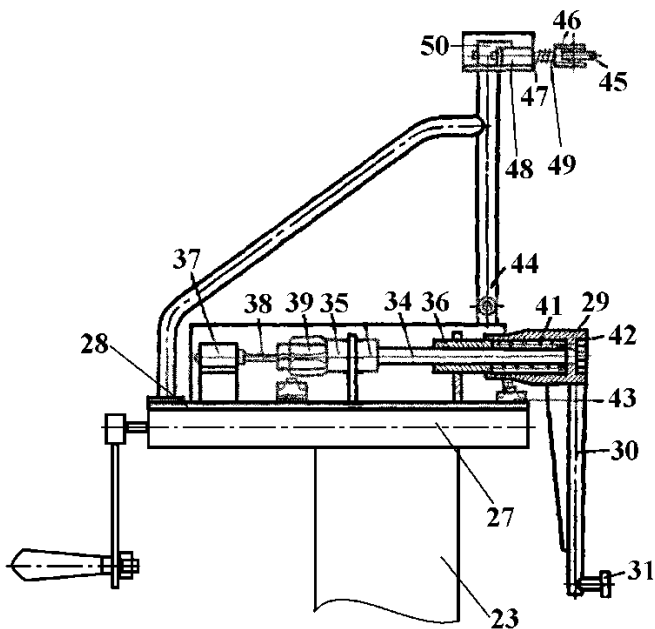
Схема приспособления для контроля и регулировки развала колес между ними, выбирая люфты в шкворневых соединениях и подшипниках ступиц управляемых колес в одном направлении:
